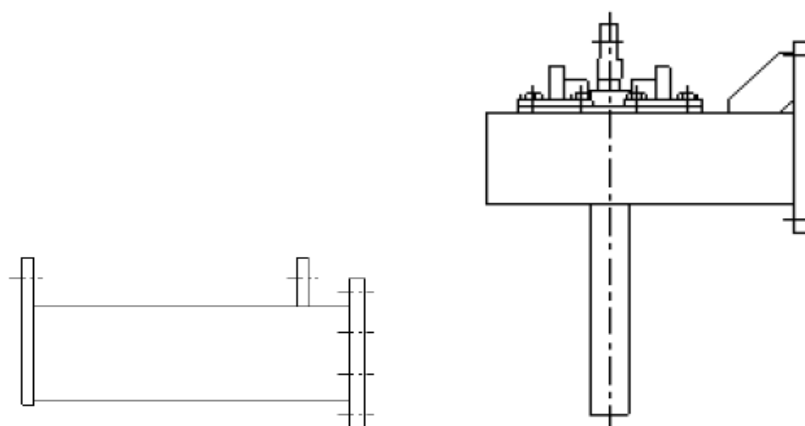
Опоры перемещения для установки боковой платформы
